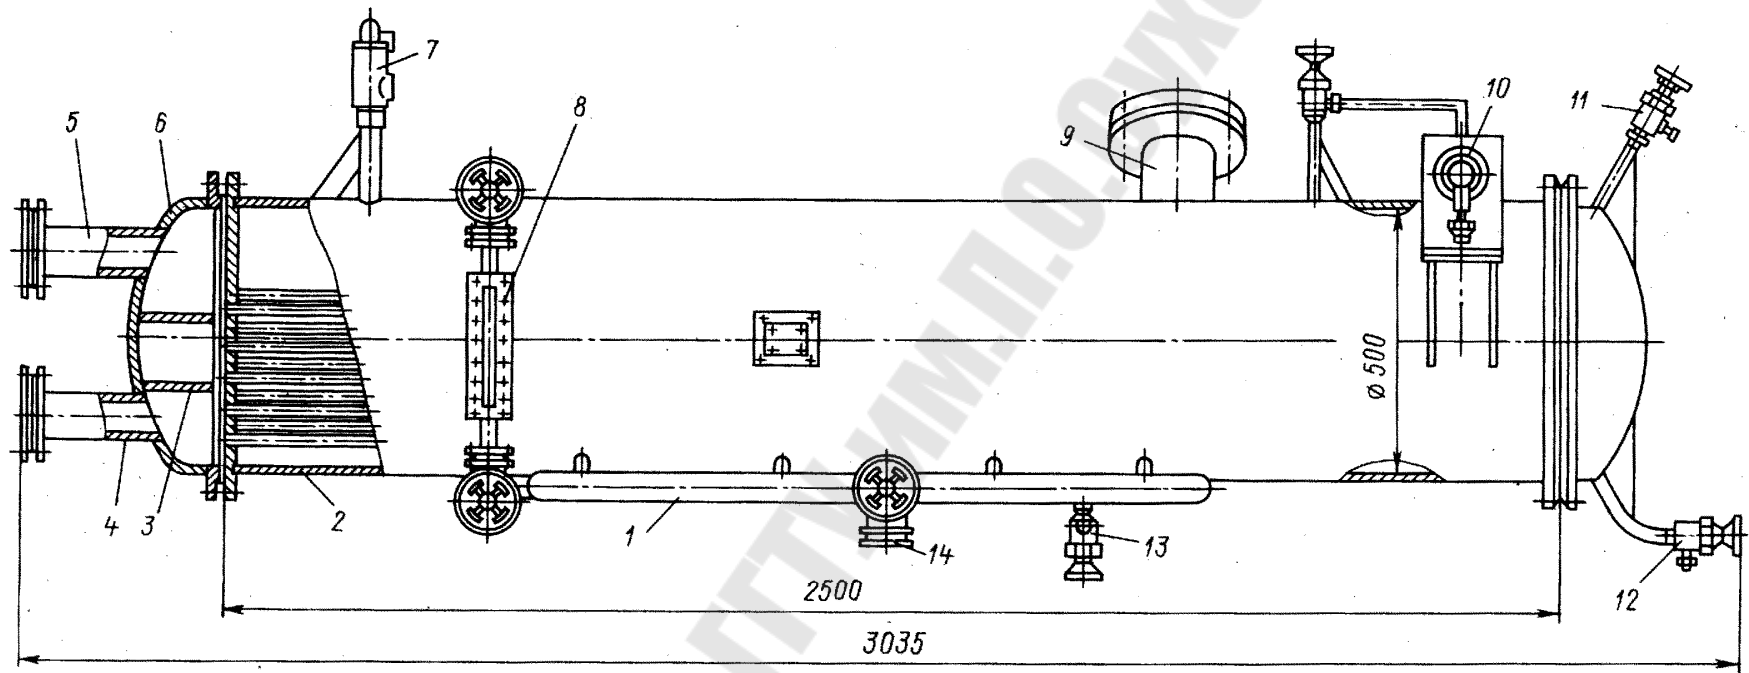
16 [16]. Фреоновый кожухотрубный испаритель затопленного типа: 1 – жидкостной коллектор; 2 – обечайка; 3 – перегородки; 4, 5 – штуцера для входа и выхода рассола; 6 – крышка; 7 – предохранительный клапан; 8 – указатель уровня; 9, 14 – штуцера для выхода и входа хладагента; 10 – манометр; 11 – кран для спуска воздуха; 12 – кран для спуска рассола; 13 – вентиль для спуска масла
